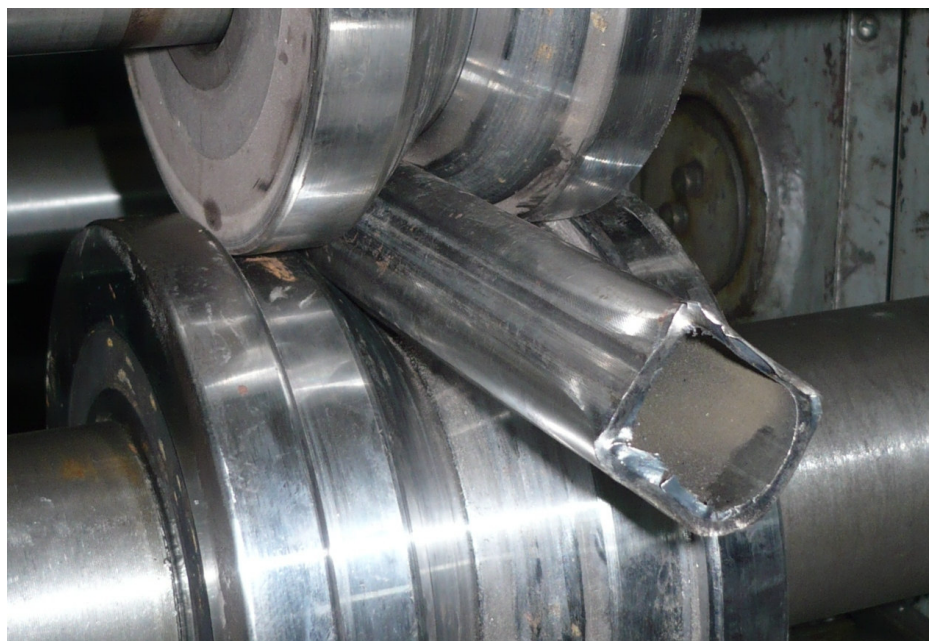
Роликовая обжимная оснастка. Процесс изготовления профиля.
